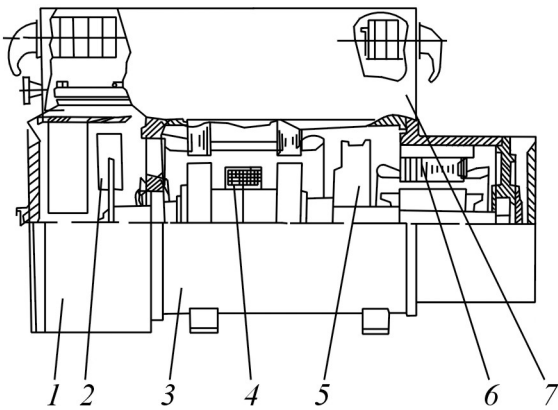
Зварювальний перетворювач ПД-305: 1 – вентиляльний блок; 2 – вентилятор; 3 – індукторний генератор; 4 – обмотка збудження; 5 – центробіжний вентилятор; 6 – електродвигун; 7 – коробка керування
